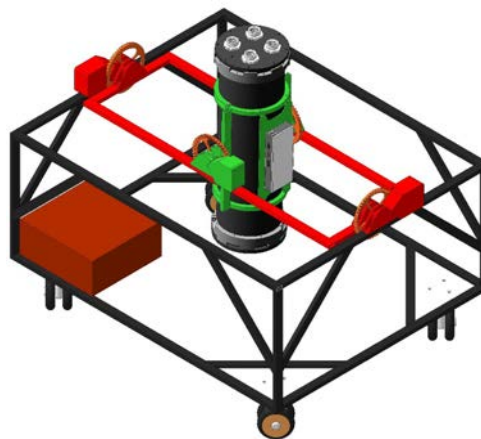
3D модель електропривода лабораторного станду 1) – міцний корпус; 2) – перша поворотна платформа; 3) – рамна конструкція станду; 4) – джерело постійного живлення 60 В; 5) – друга поворотна платформа; 6) – крокові двигуни; 7) – шестерні; 8) – опорні полиці; 9) – ребра міцності; 10) – колісна база; 11) – поворотний хомут
